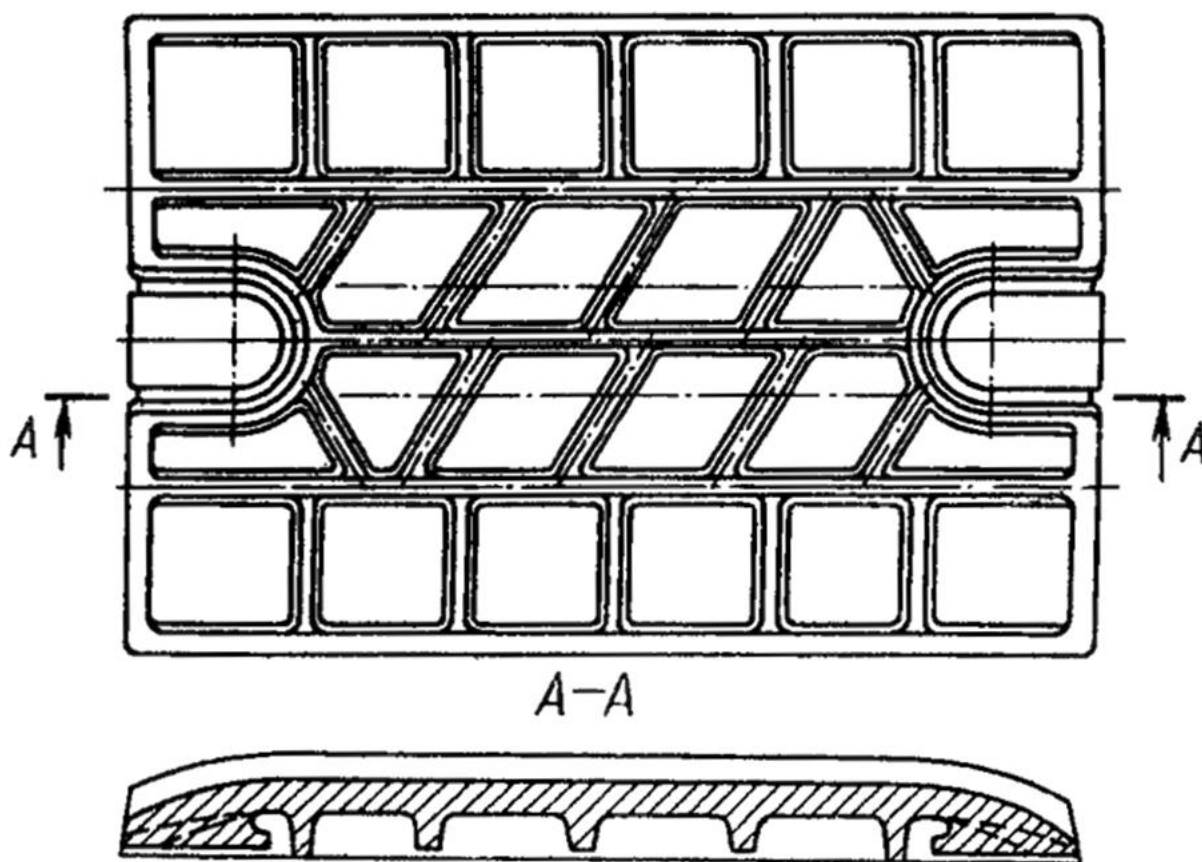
Конструкція дробильної плити щокової дробарки
